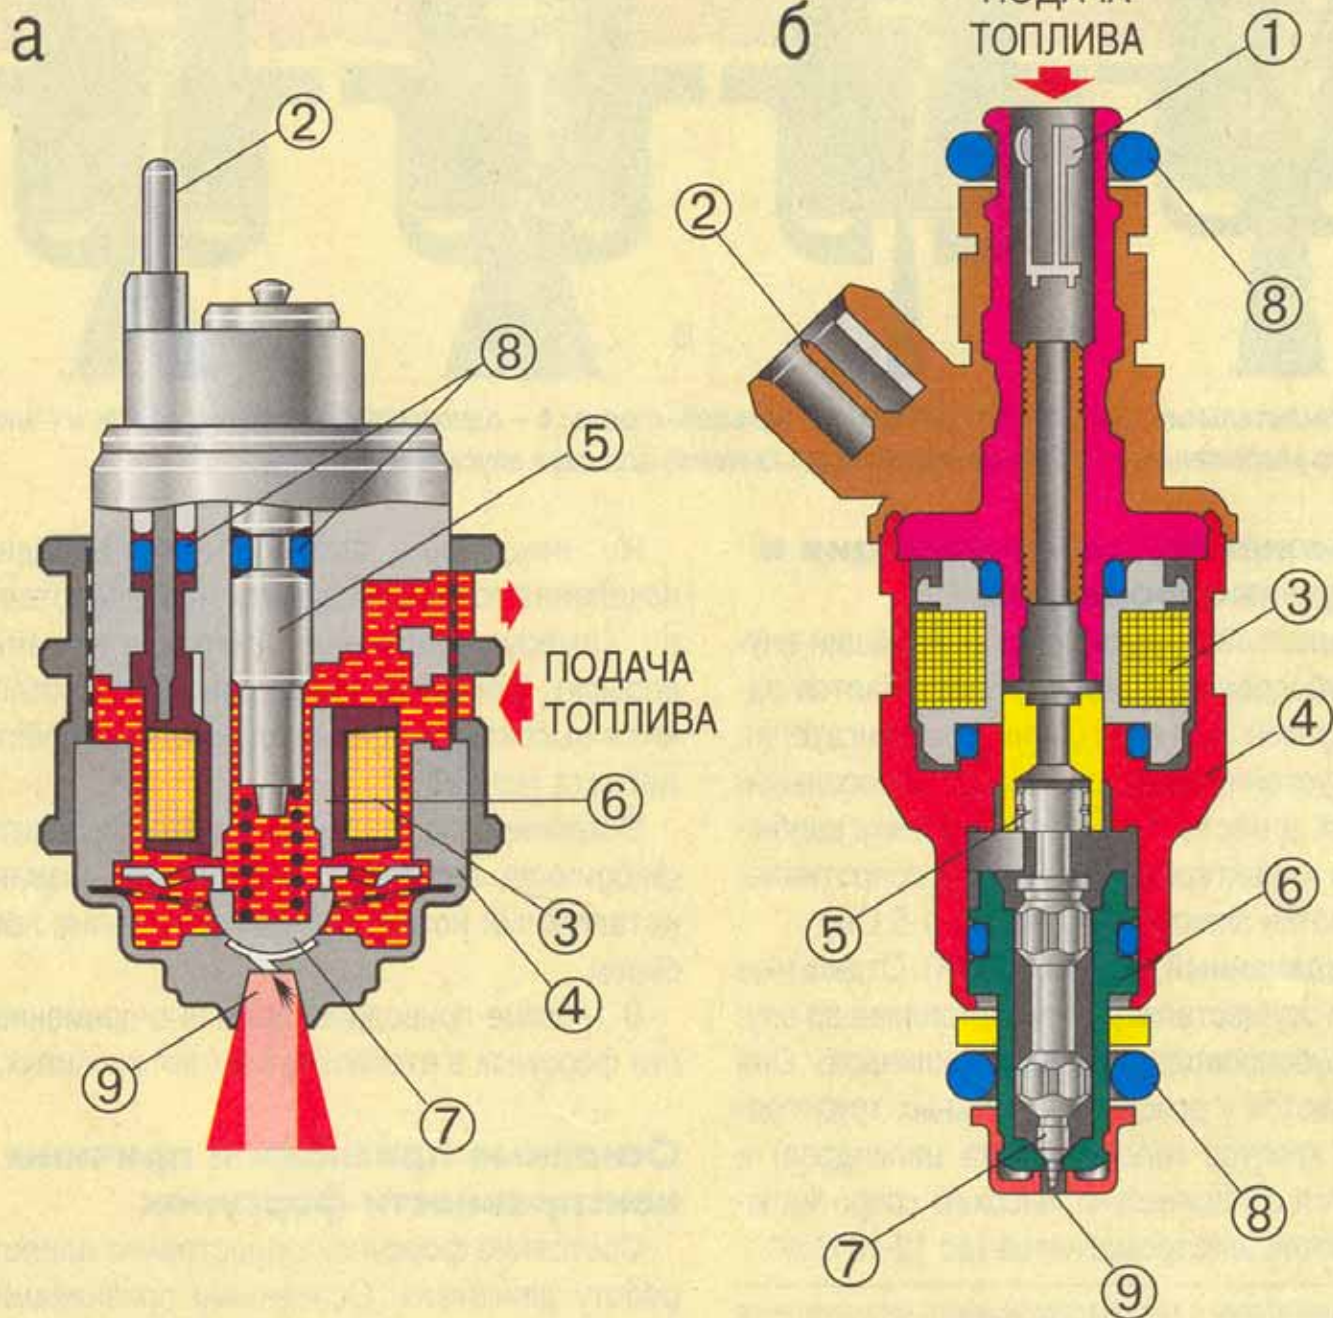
Устройство форсунки: а – форсунка центрального впрыска; б – форсунка распределенного впрыска; 1 – фильтр; 2 – электрический разъем; 3 – обмотка электромагнита; 4 – корпус форсунки; 5 – сердечник; 6 – корпус клапана (а), корпус клапана (б); 7 – клапан (а), игла клапана (б); 8 – уплотнительное кольцо; 9 – распылительное отверстие.
